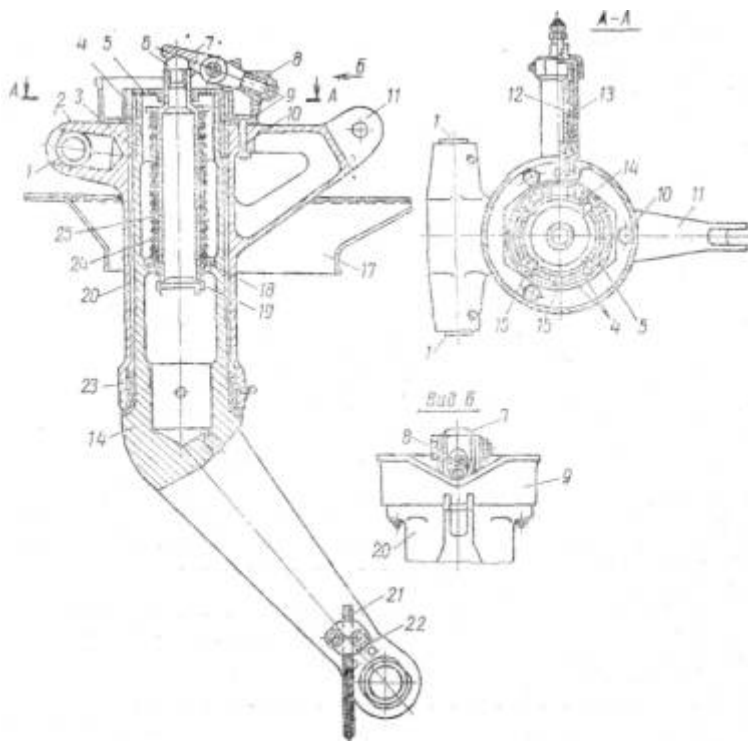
Траверса и вилка установки хвостового колеса:
